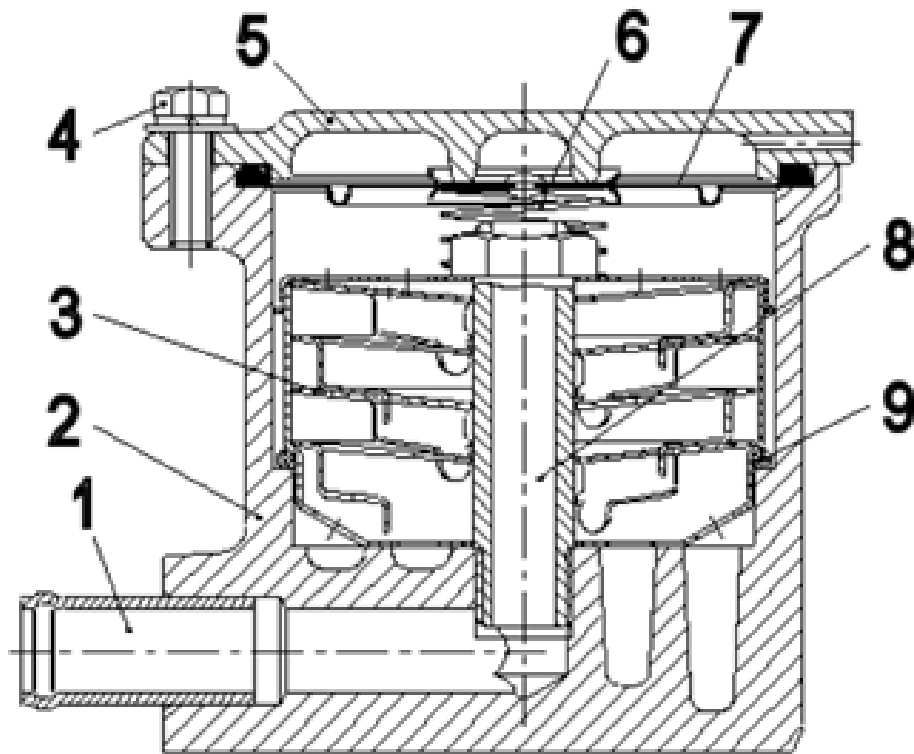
Масловідділювач двигуна ЯМЗ: 1 - вихідний патрубок;
